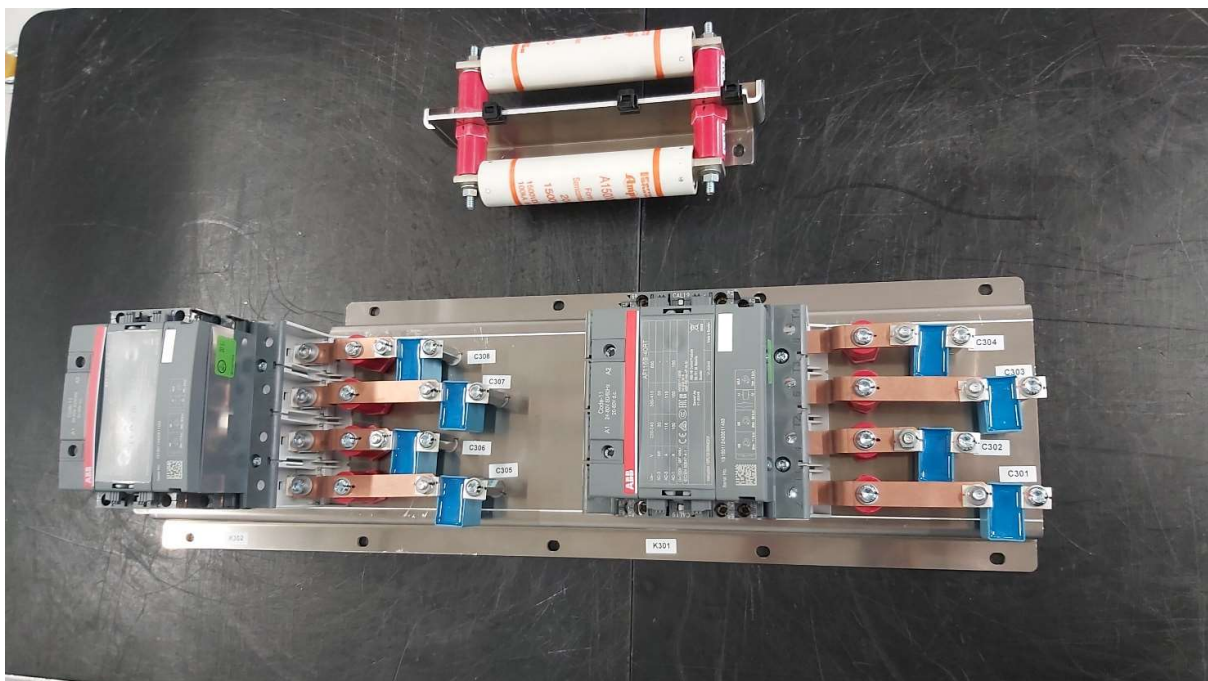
Due sottoassiemi meccanici: si nota la differenza di dimensione e di complessità costruttiva
